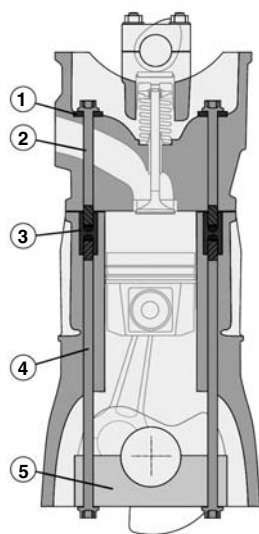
Болтовое соединение головки блока цилиндров длинными стяжными болтами:
